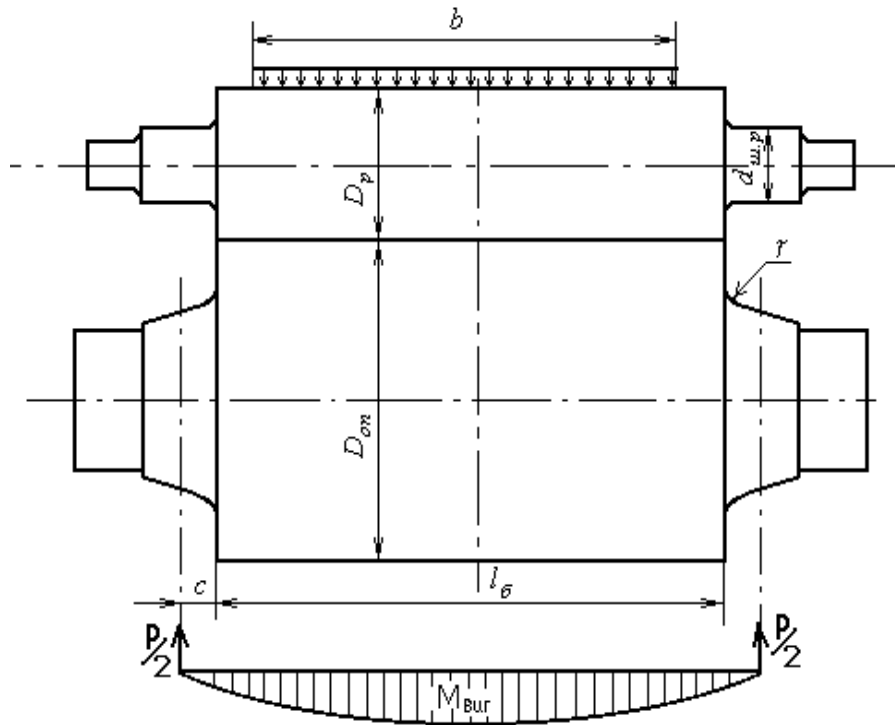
Розрахункова схема валків кліті кварто
